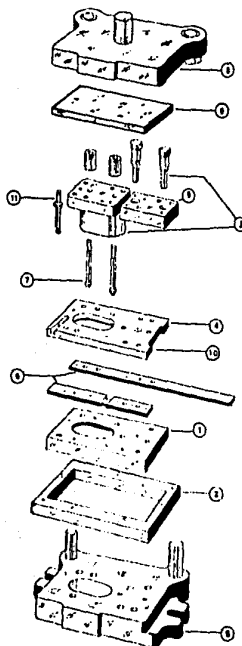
EXPLOSIVO DE PARTES DE UN TROQUEL.
